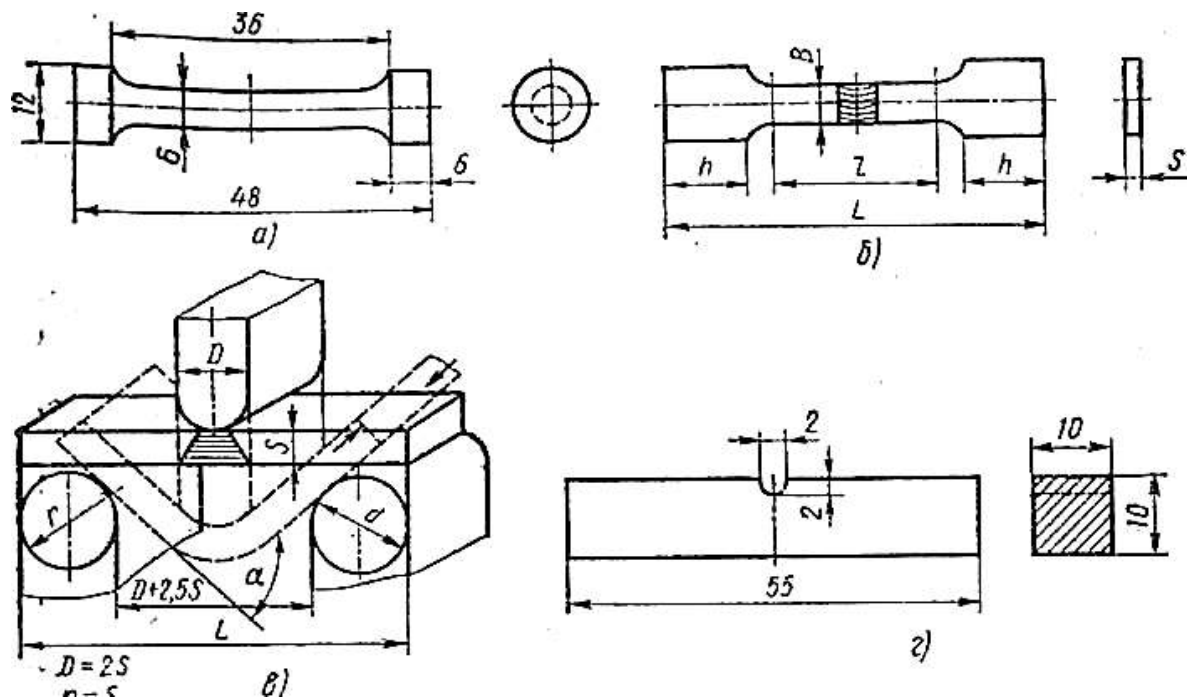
Образцы для определения механических свойств: а, б — на растяжение наплавленного металла (а) и сварного соединения (б), в — на изгиб, г — на ударную вязкость
